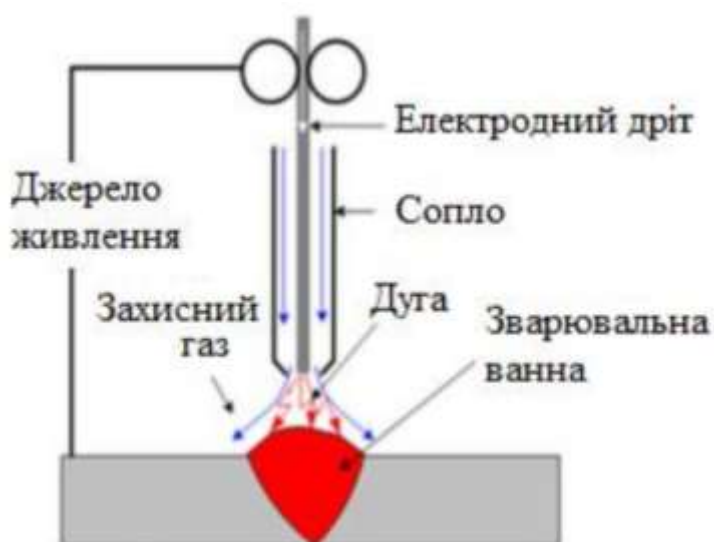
Схема автоматичного зварювання у суміші захисних газів
